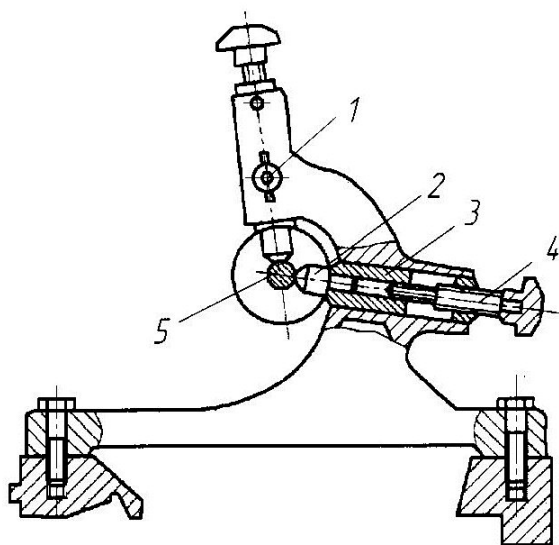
Подвижный люнет: 1 — стопор; 2 — кулачок; 3 — держатель кулачка; 4 — винт регулировочный; 5 — заготовка
